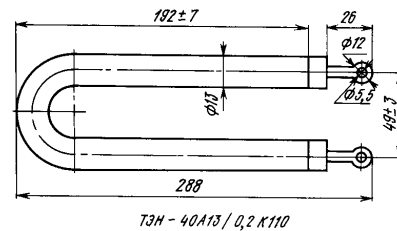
Габаритные, установочные и присоединительные размеры ТЭНа 40А13/0,2К110
